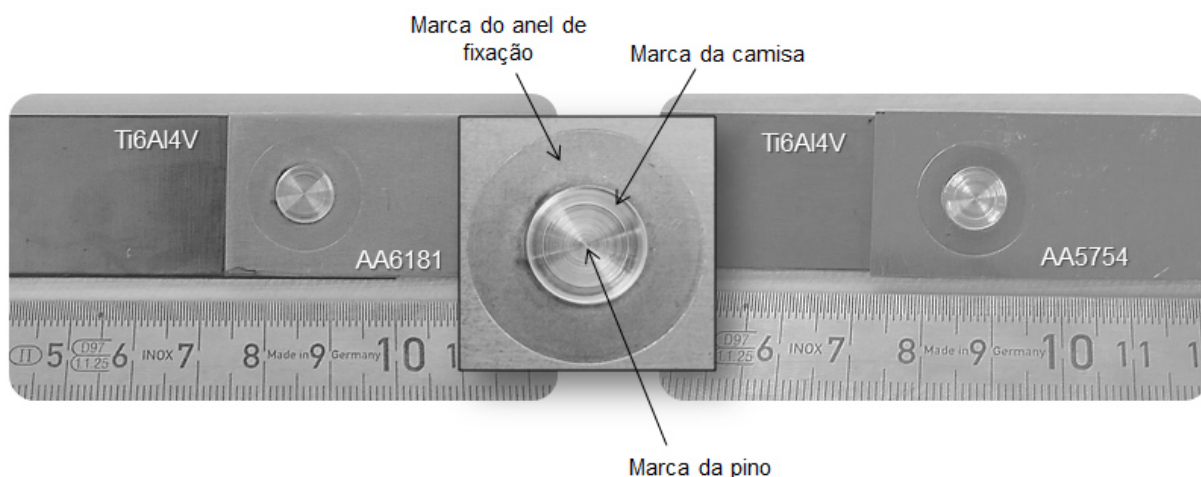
Juntas dissimilares sobrepostas soldadas pelo processo FSpW.
